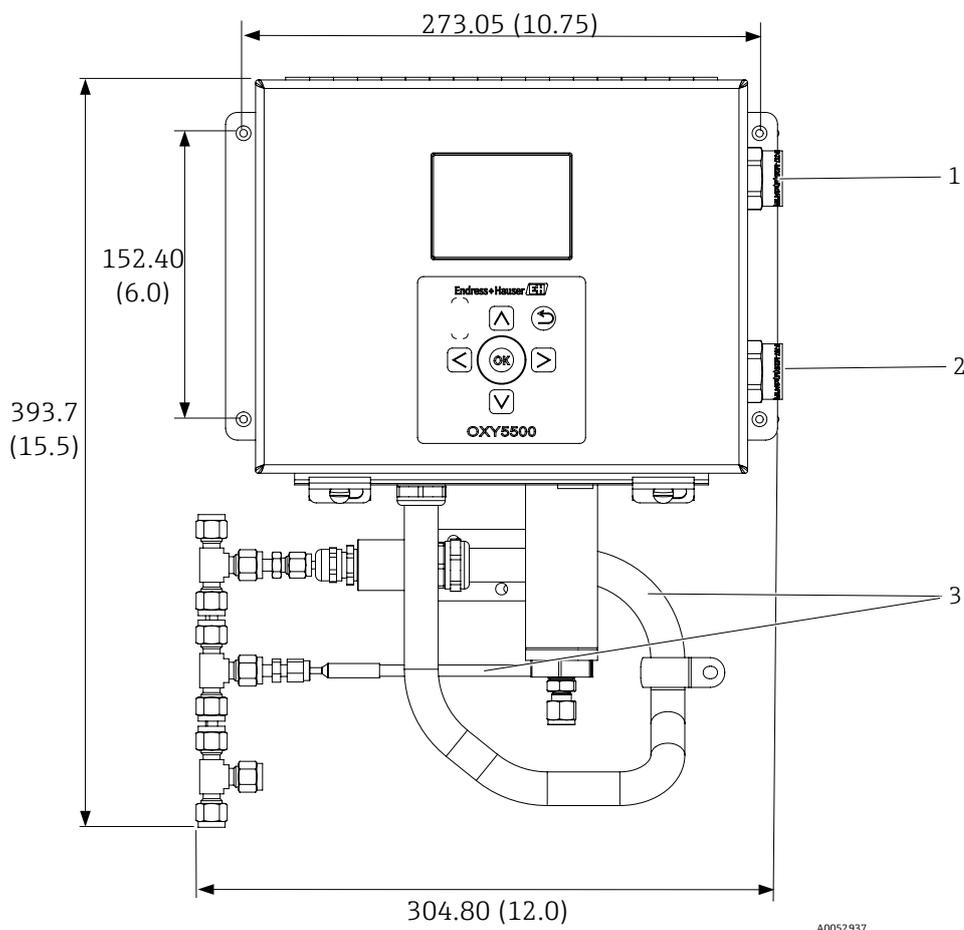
Schema e dimensioni di montaggio - montaggio a fronte quadro. Dimensioni: mm (in.)
